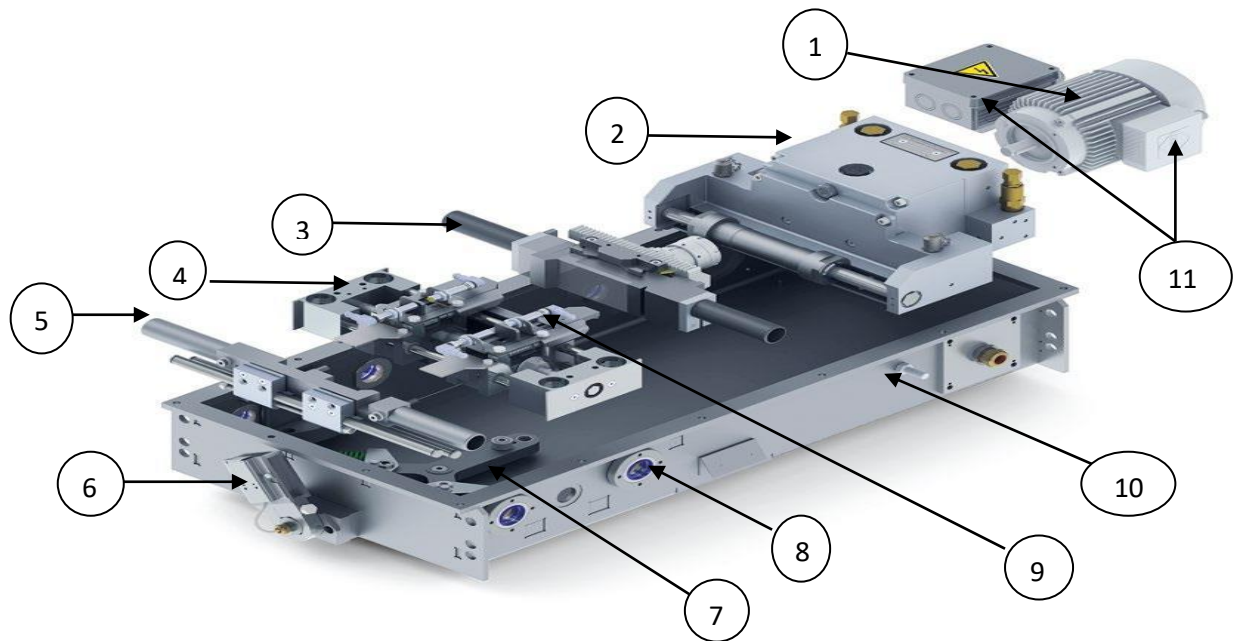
Vue du principal sous-groupe moteur sans couvercle [15]
